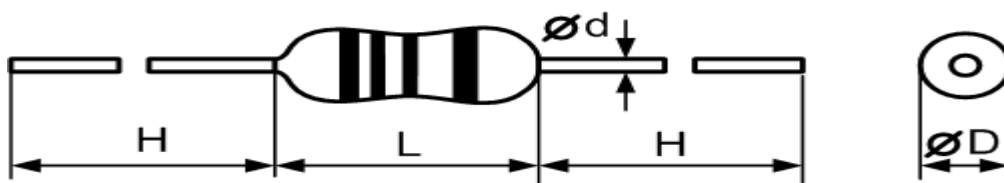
Габаритні розміри резистора АСС (R1-R3, R5-R10, R12-R24)
